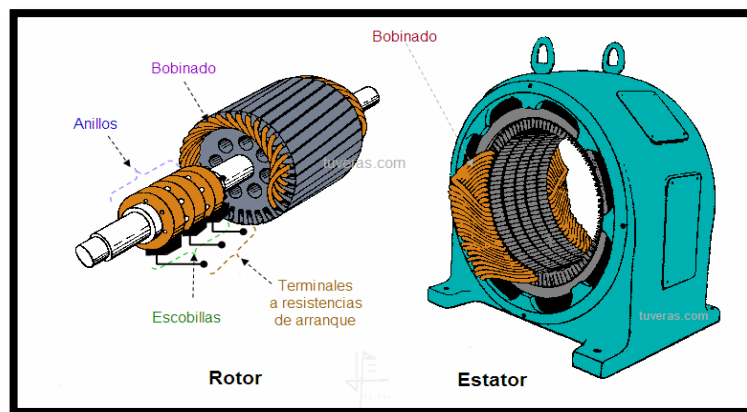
16 Motor Asíncrono de Rotor Bobinado.
